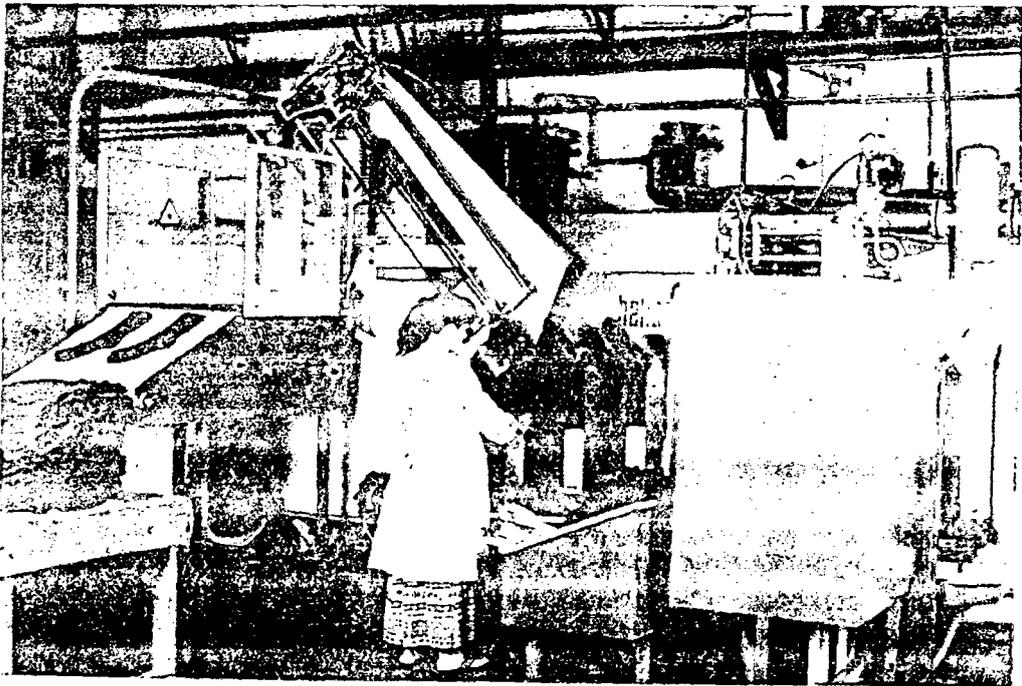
PLANCHA No. 4 MARCA HELIOT
